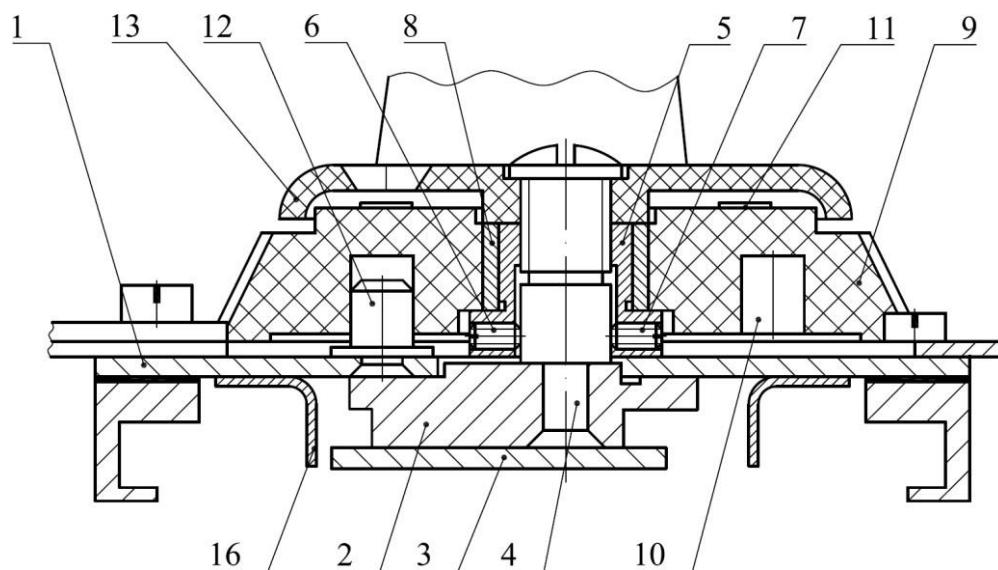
Конструктивна схема пристрою зміни глибини кулірування.
